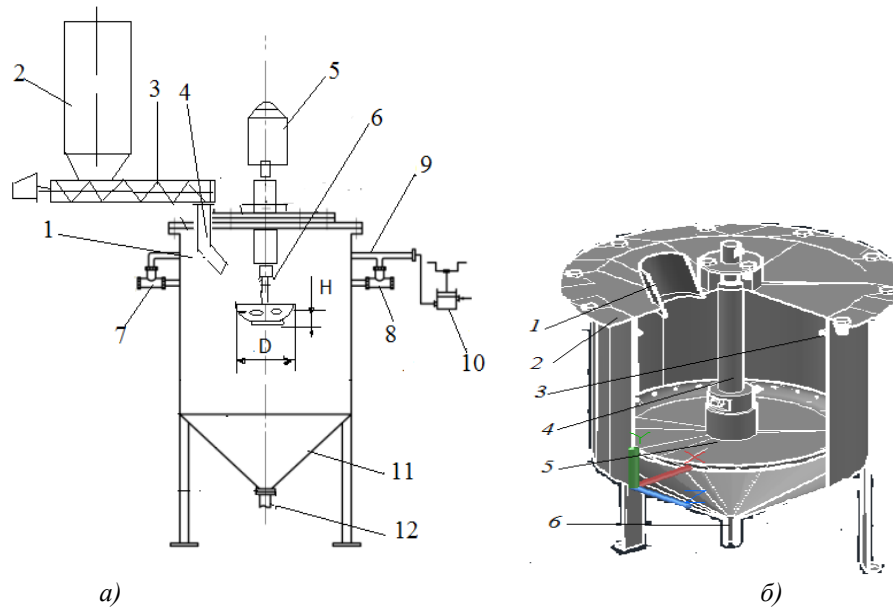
Схема змішувача (а) та 3Д – модель змішувача (б): 1 – патрубок для дозуючого борошна; 2 – кришка циліндричної робочої камери; 3 – сопло для розпилювання рідких компонентів; 5 – тарільчастий робочий орган; 6 – патрубок вивантаження змішаної суміші
